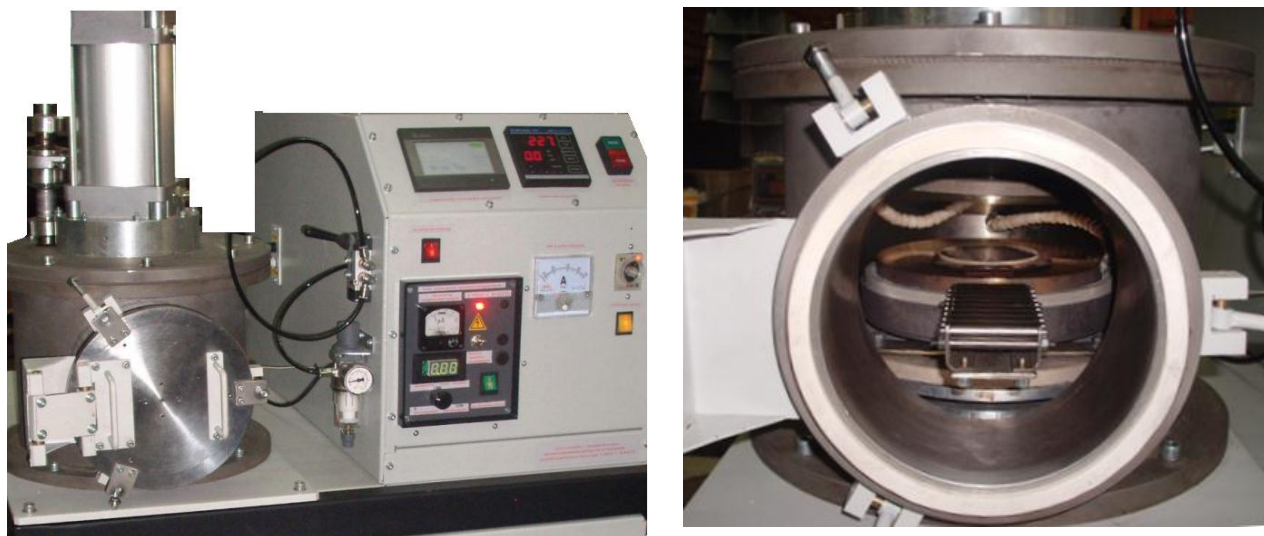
Опытно-промышленная установка анодной сварки
